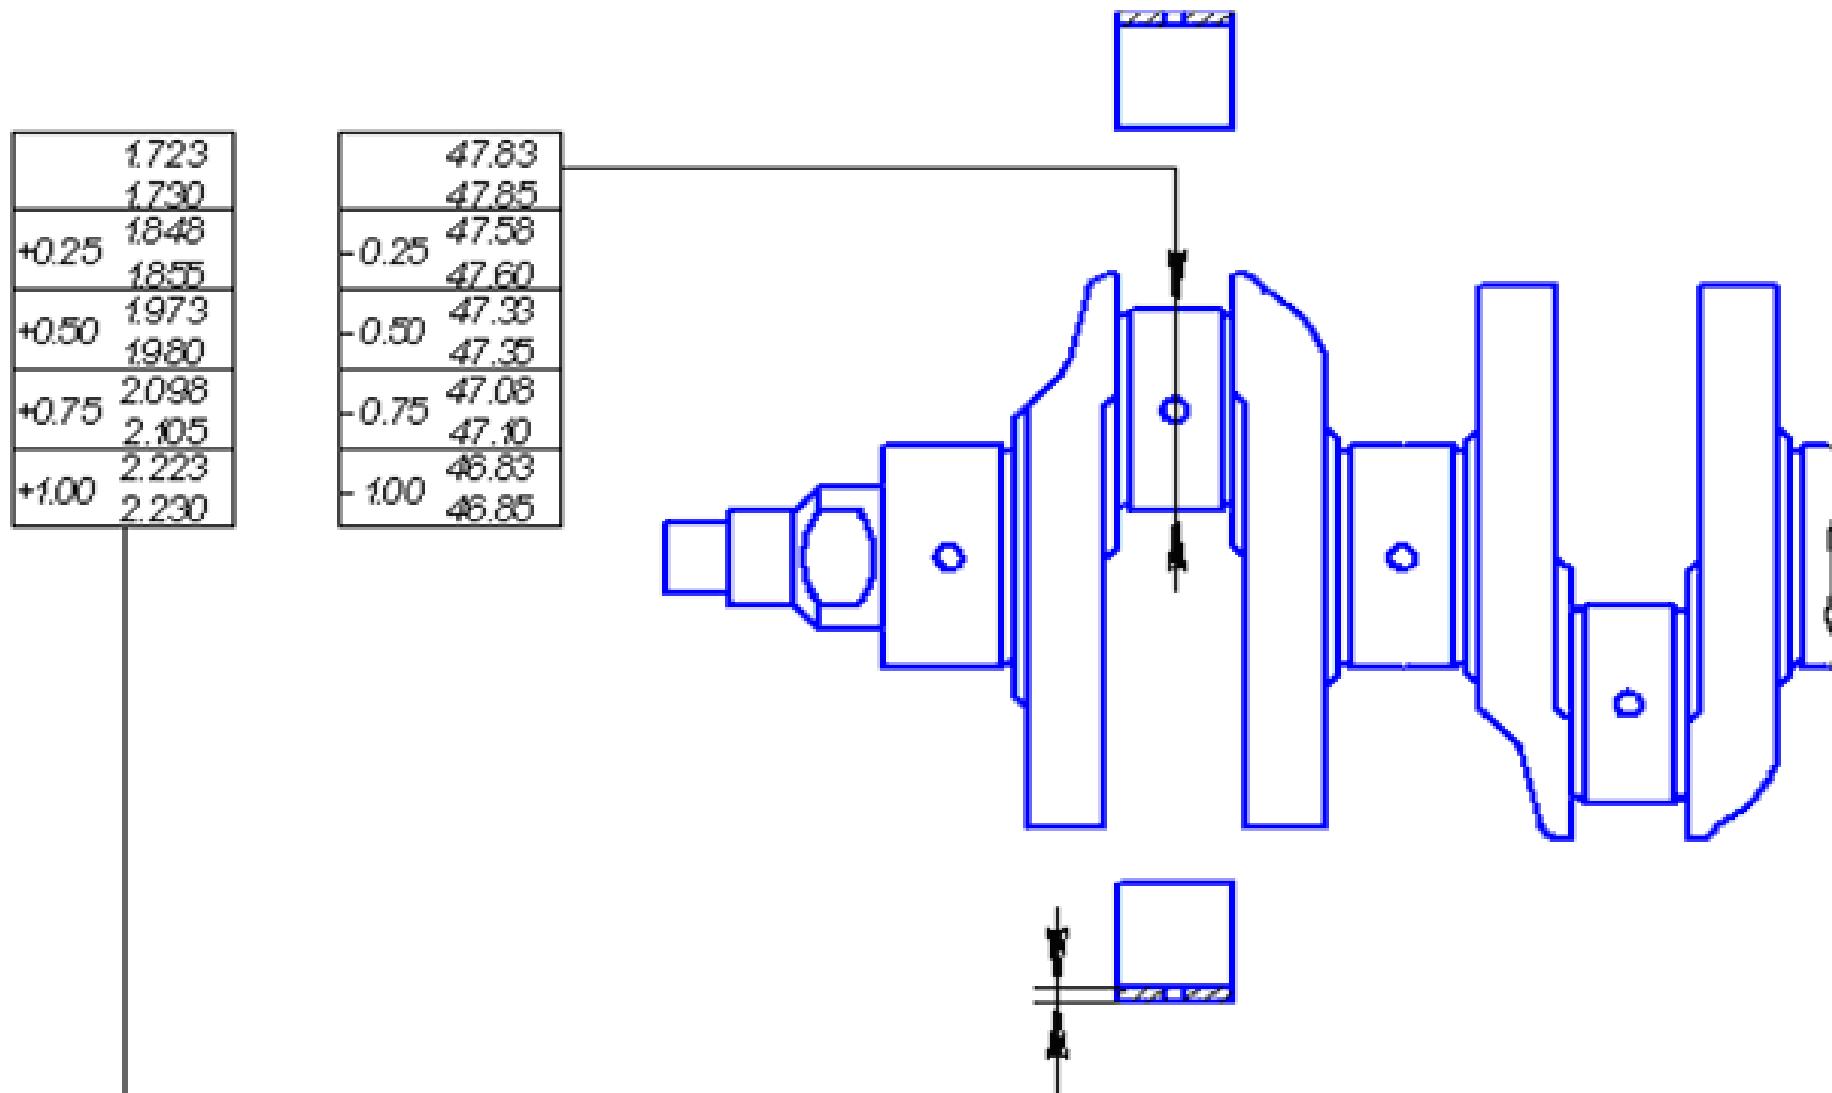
Основные размеры коленчатого вала автомобиля ВАЗ шатунных шеек
